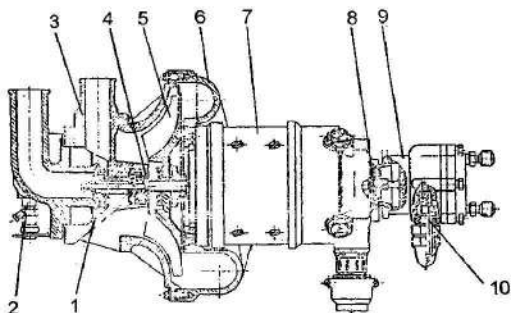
Насосный агрегат: 1 - крыльчатка жидкостного насоса; 2 - сливной кран; 3 - жидкостный насос; 4 - манжета; 5 - крыльчатка вентилятора; 6 - корпус вентилятора; 7 - электродвигатель; 8 - соединительная муфта; 9 - топливный насос; 10 - редукционный клапан.
